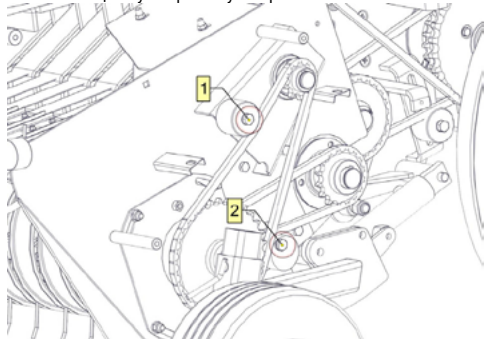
Регулировка натяжения цепей пресс-подборщика.
